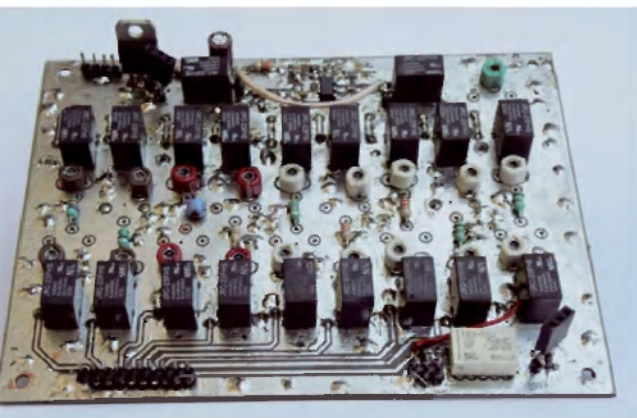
Rysunek płytki PCB z rozmieszczeniem elementów
